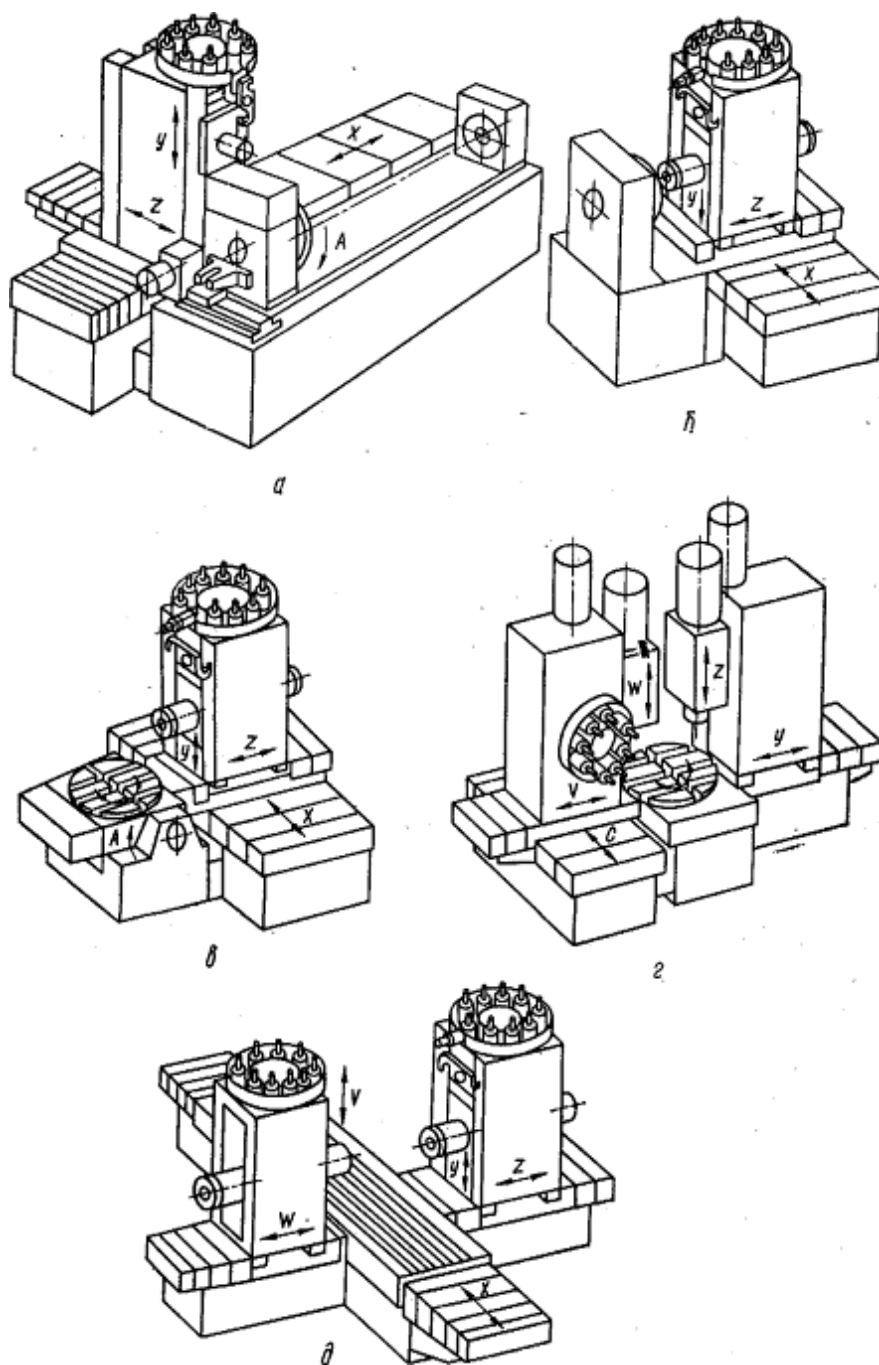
Типовые компоновки обрабатывающих центров
